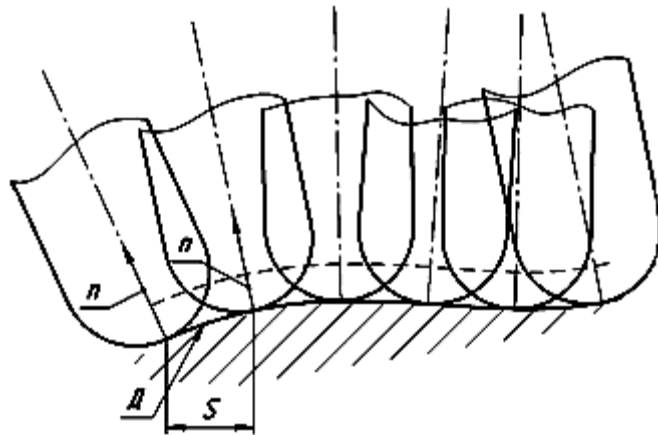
Схема обробки на 5-ти координатному верстаті [13]
